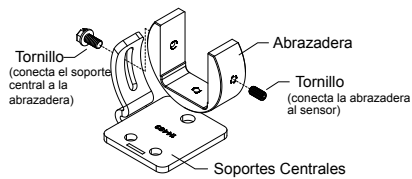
Accesorios para el soporte de montaje central de MINI-ARRAY
